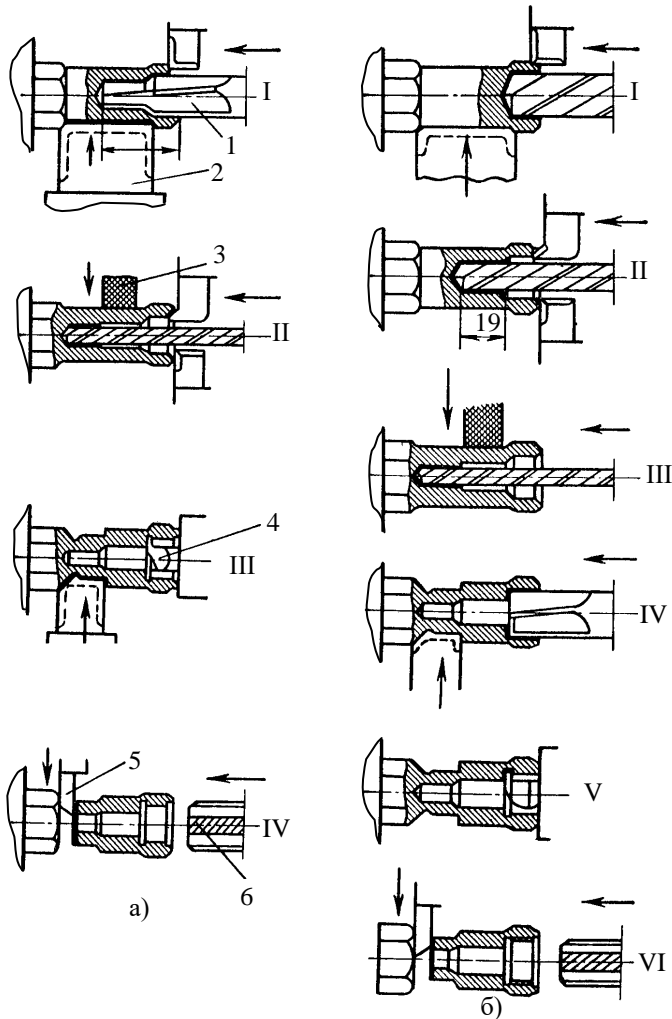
Налаштування чотири- (а) та шестишпindelного (б) автоматів для обробки корпусу свічки двигуна: I-VI – номери шпindelів
